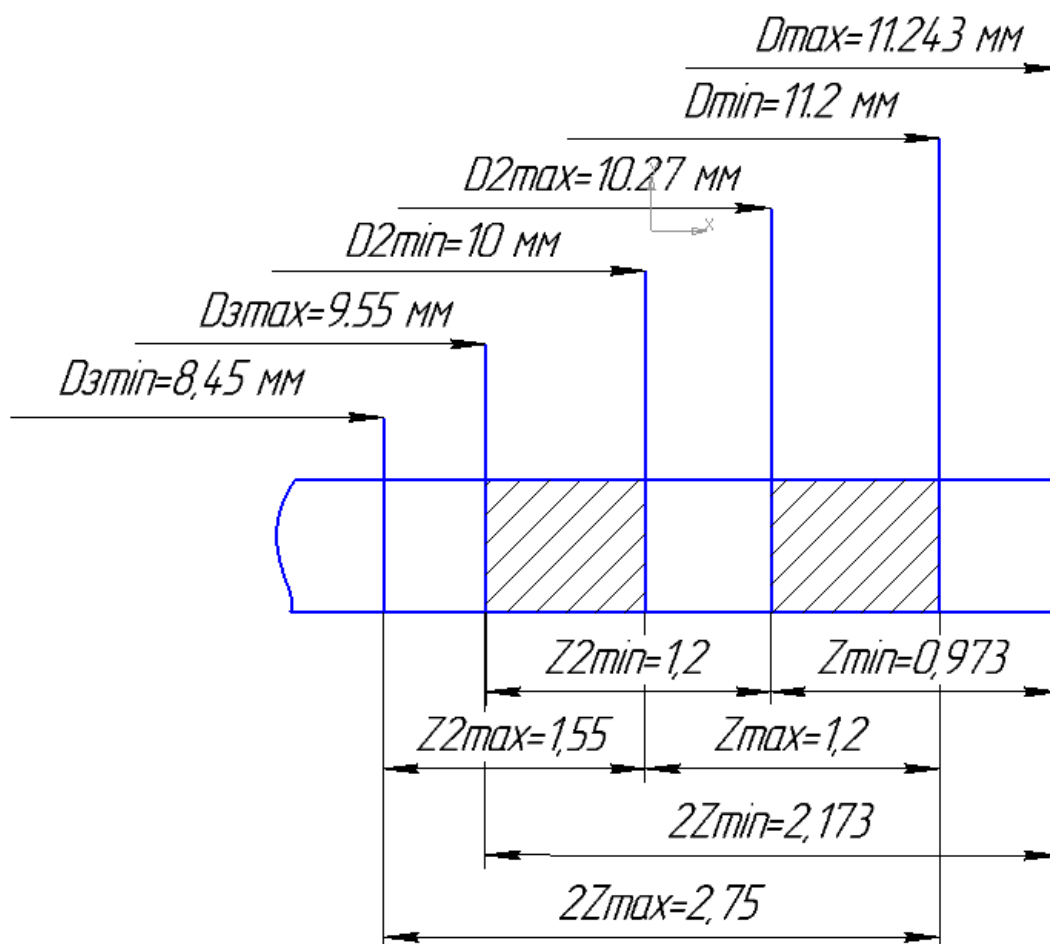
Схема розташування полів допусків і припусків на обробку поверхні під різьбу М12-7Н.
